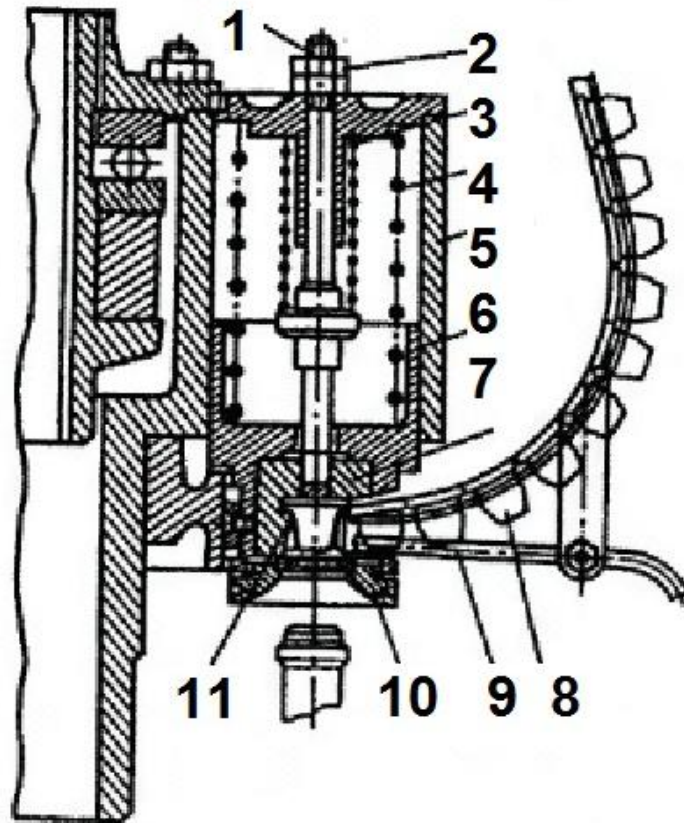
Механізм для закупорювання поліетиленовими пробками
